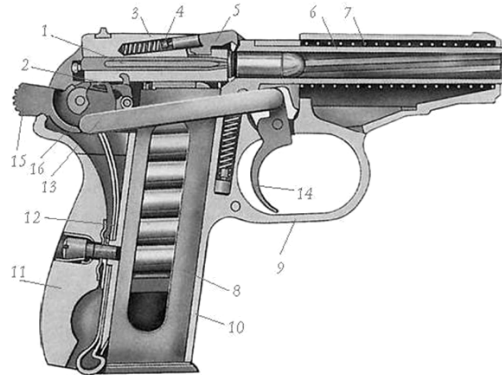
Основні частини пістолета Макарова: 1 – ударник; 2 – шептало; 3 – затвор; 4 – пружина викидача; 5 – викидач; 6 – ствол; 7 – зворотна пружина; 8 – магазин; 9 – спускова скоба; 10 – рамка; 11 – рукоятка; 12 – бойова пружина; 13 – спускова тяга; 14 – спусковий гачок; 15 – курок; 16 – важіль взводу.
